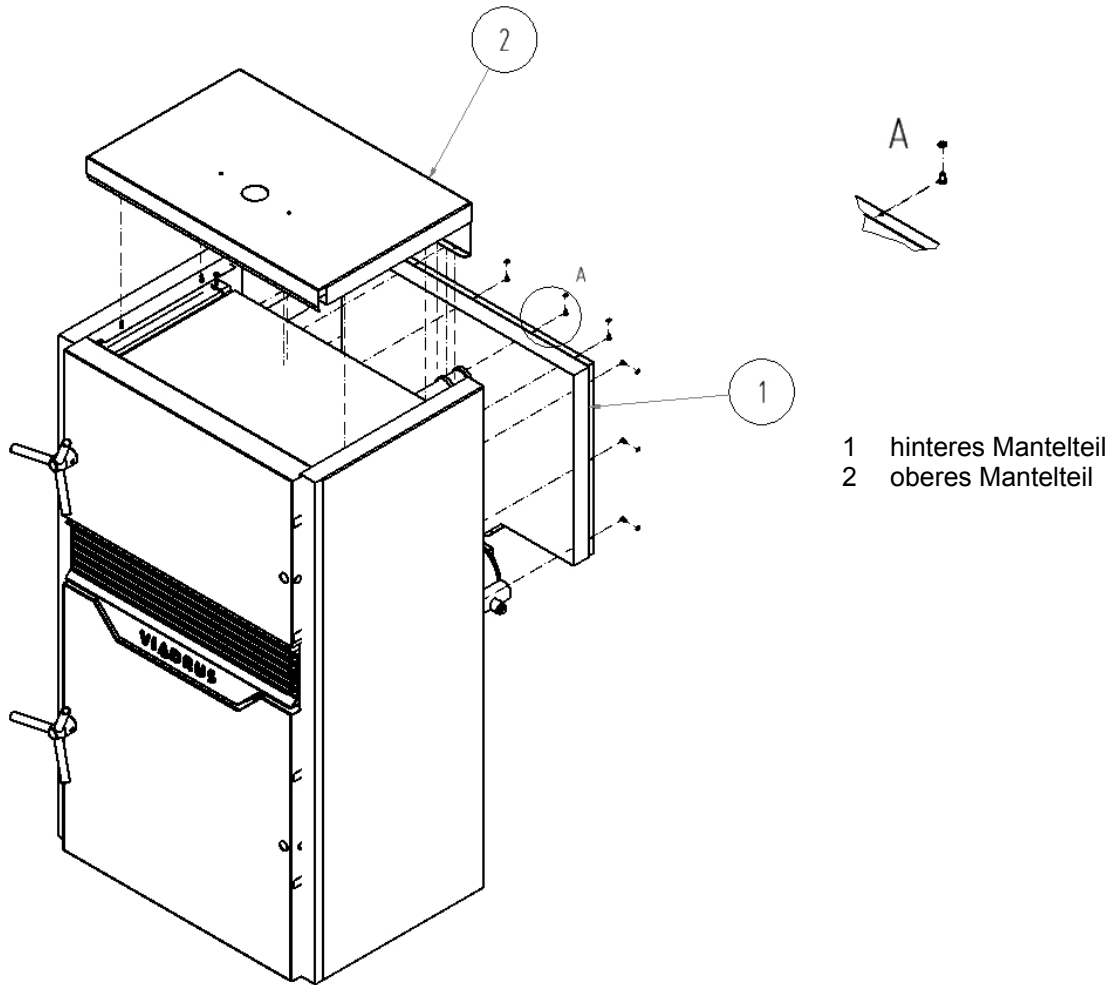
Demontage des oberen und hinteren Mantelteils
